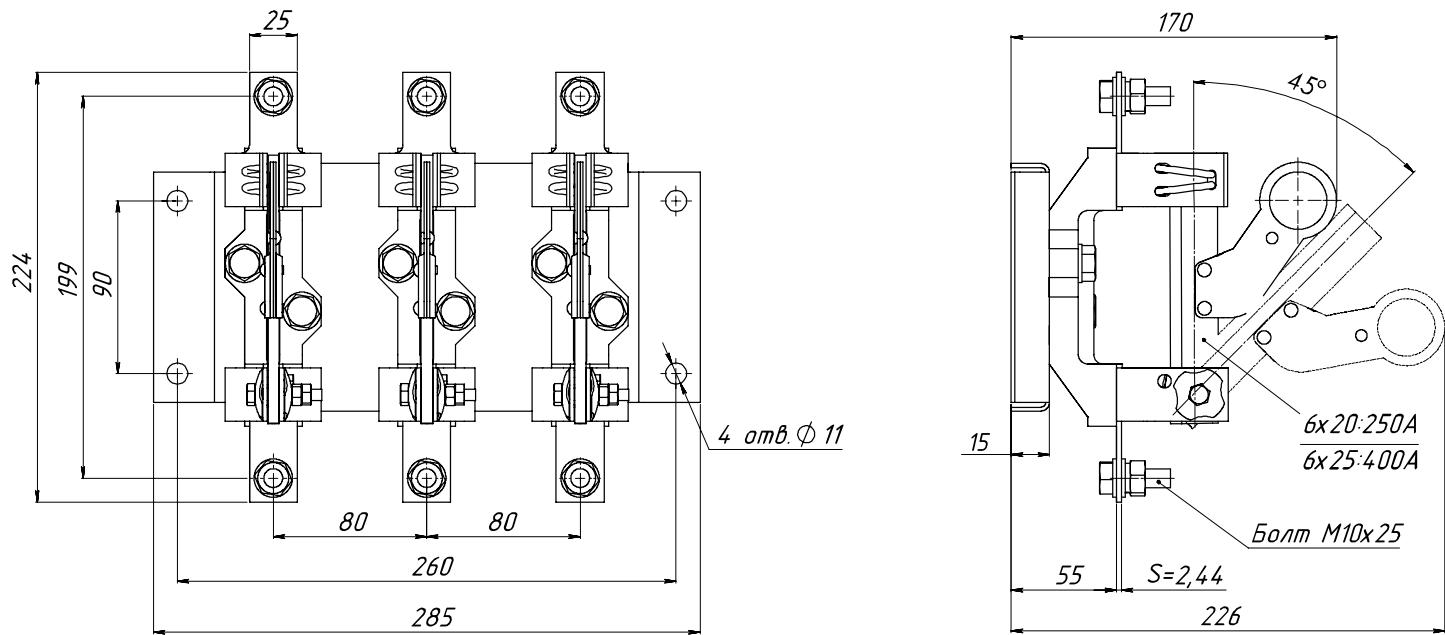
Разъединитель РЕ19-35(37)-31160-00 УХЛЗ с рычагом для пополюсного оперирования штангой
